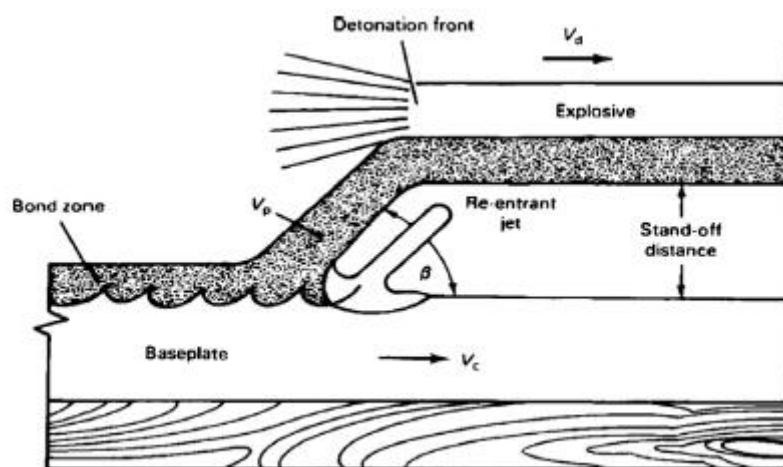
Schema des Explosionsschweißens [66]
